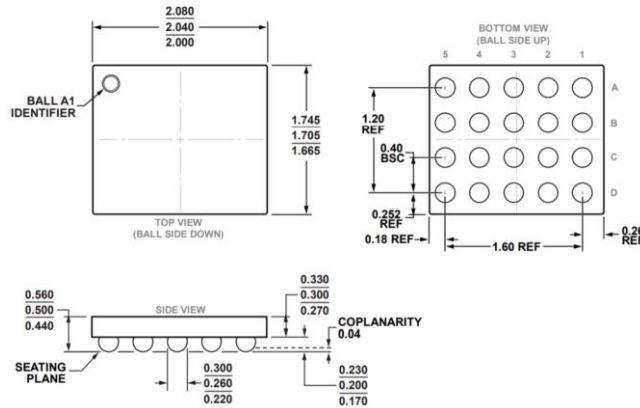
Footprint y dimensiones del microchip AD8233 estructura 20 pin LFCSP dimensión 2.0x1.7mm.
